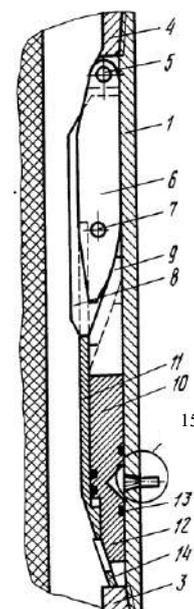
Центратор гидравлический [3]: 1 – обсадная труба; 2 – отверстия; 3, 4 – муфты; 5 – пальцы; 6 – пары рычагов; 7 – оси; 8 – центрирующий башмак; 9 – клинья; 10 – поршень; 11 – цилиндры; 12 – замковый поршень; 13 – резиновые кольца; 14 – замковые кольца; 15 – срезная пробка
